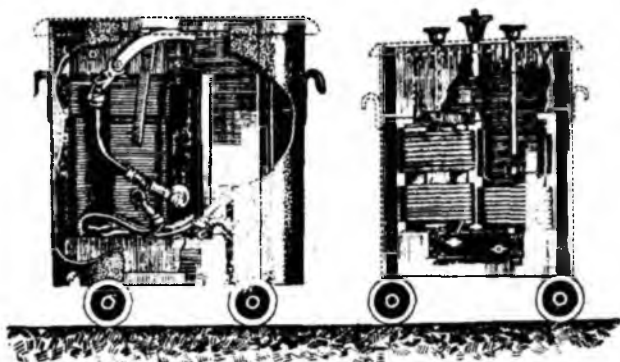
Сварочный трансформатор СТ-2.
